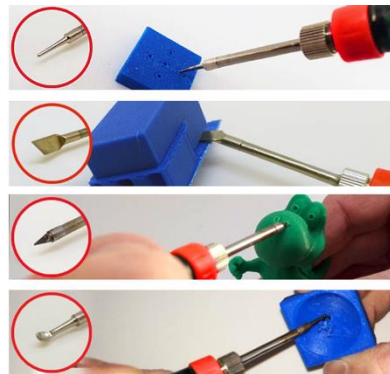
PostProcesado Usando un Soldador de Estaño
